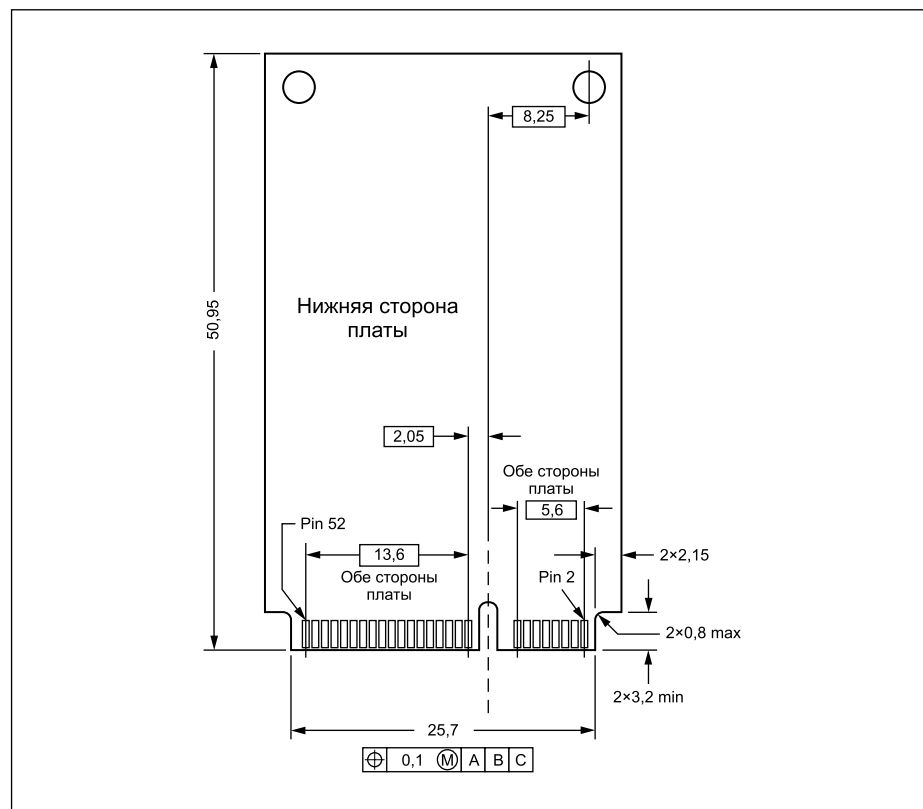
Габаритные размеры платы, регламентированные стандартом PCI Express Full-Mini Card
